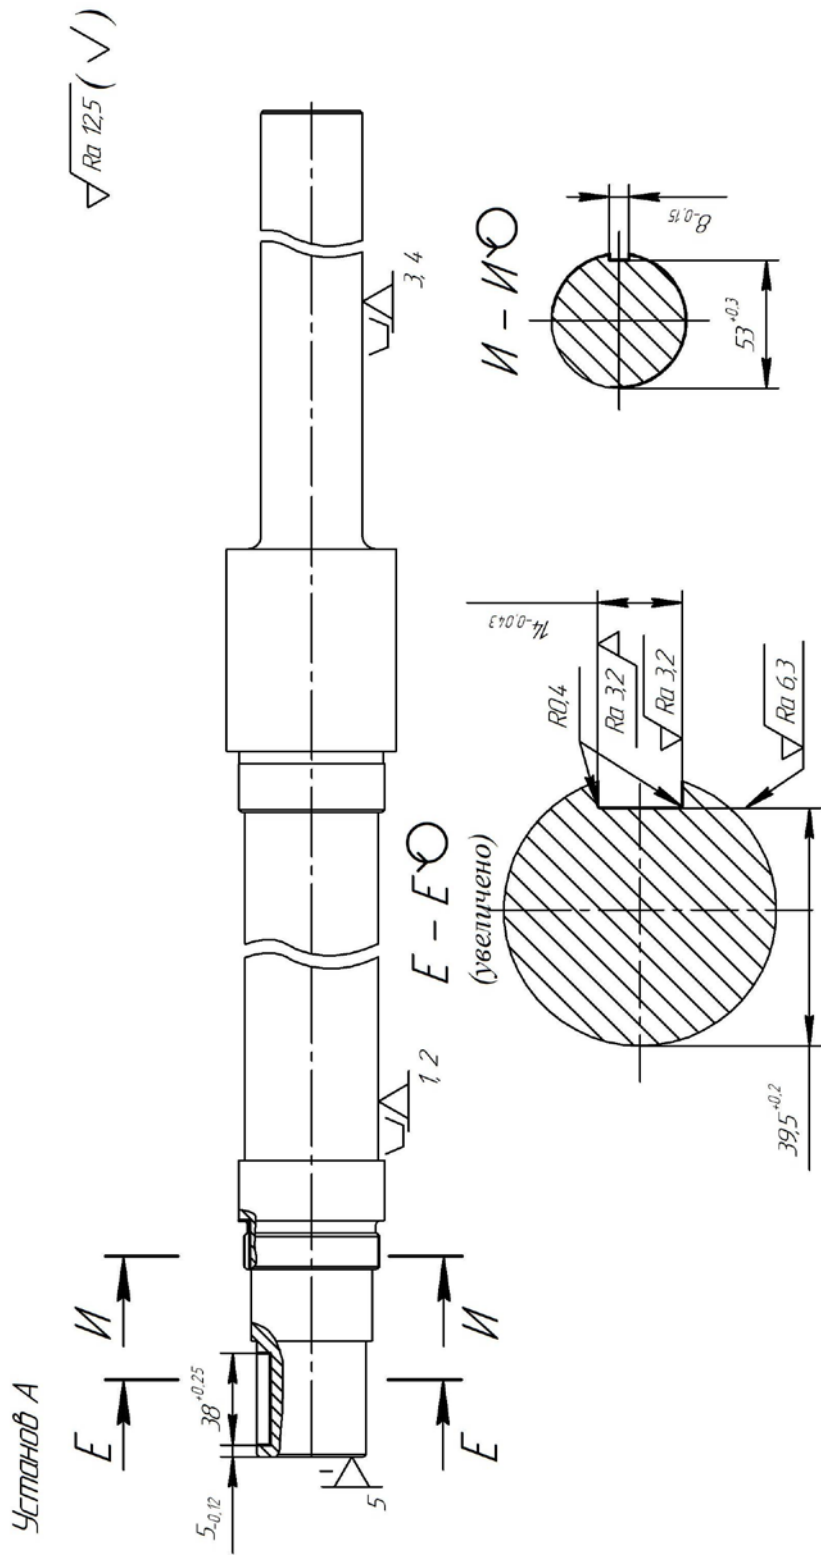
Схема базування заготовки на операції фрезерній 030, установ А
